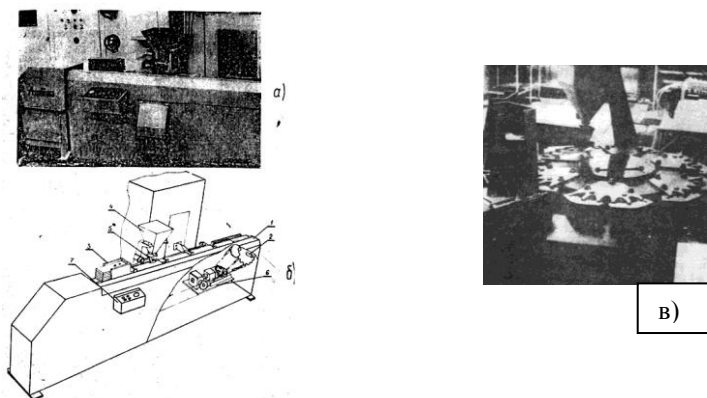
Линия для наплавки полевой доски (а) и ее схема (б);
